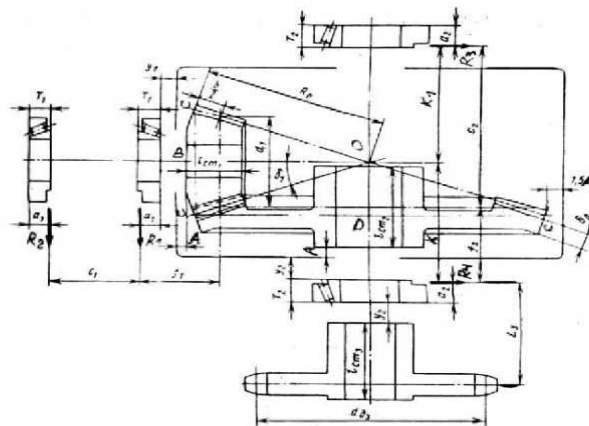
Схема предварительной компоновки одноступенчатого конического редуктора
